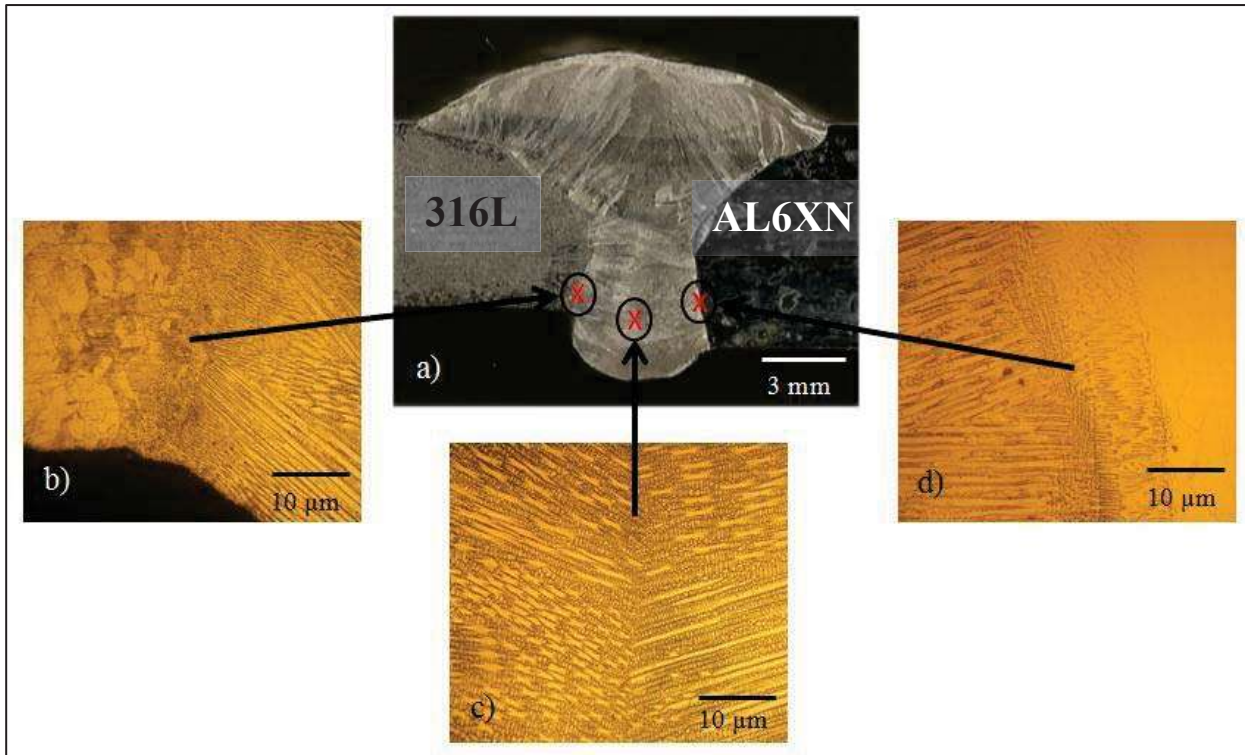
a) Macrografía de la unión soldada, b) micrografía de la región 316L – soldadura, c) micrografía del centro del cordón de soldadura, d) micrografía de la región soldadura – AL6XN.
